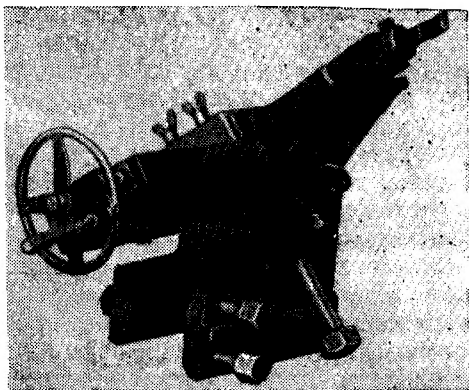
Приспособление для обточки коллекторов тяговых двигателей под электровозом
